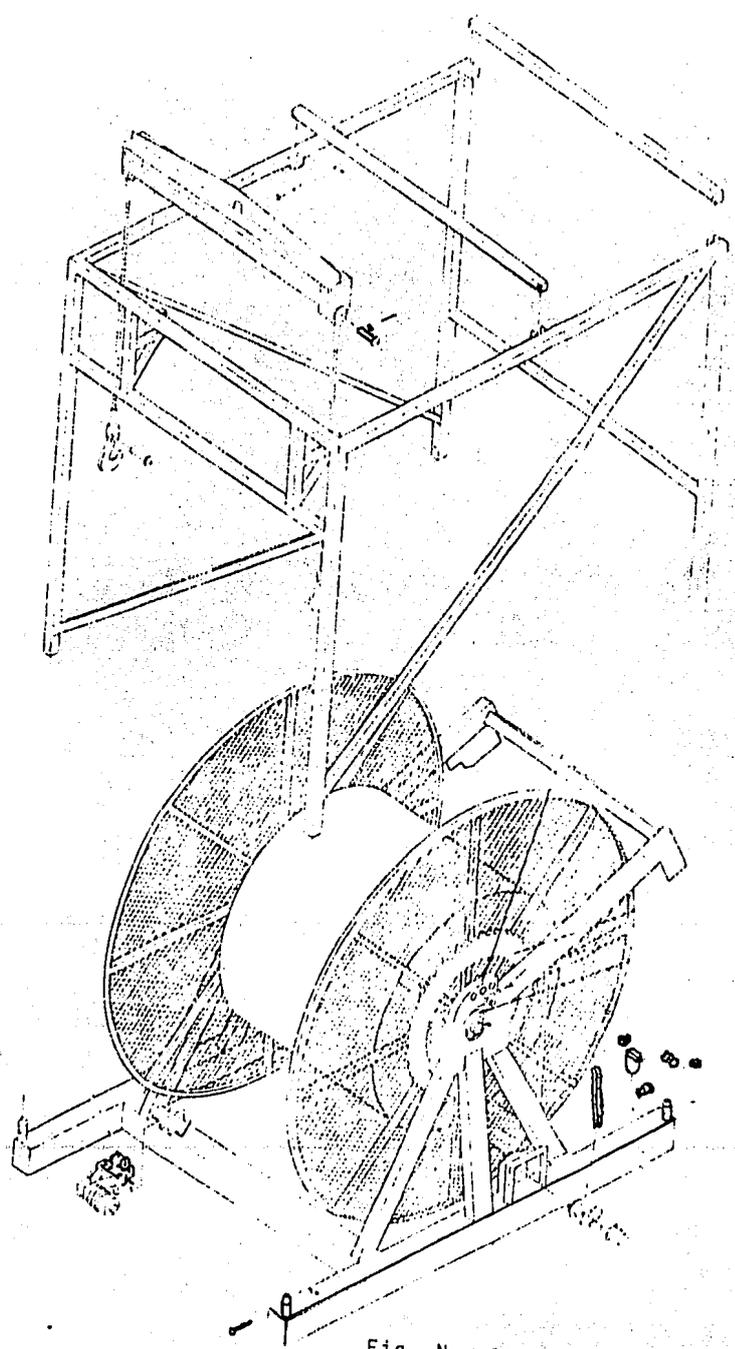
ESTRUCTURA DEL CARRETE.
